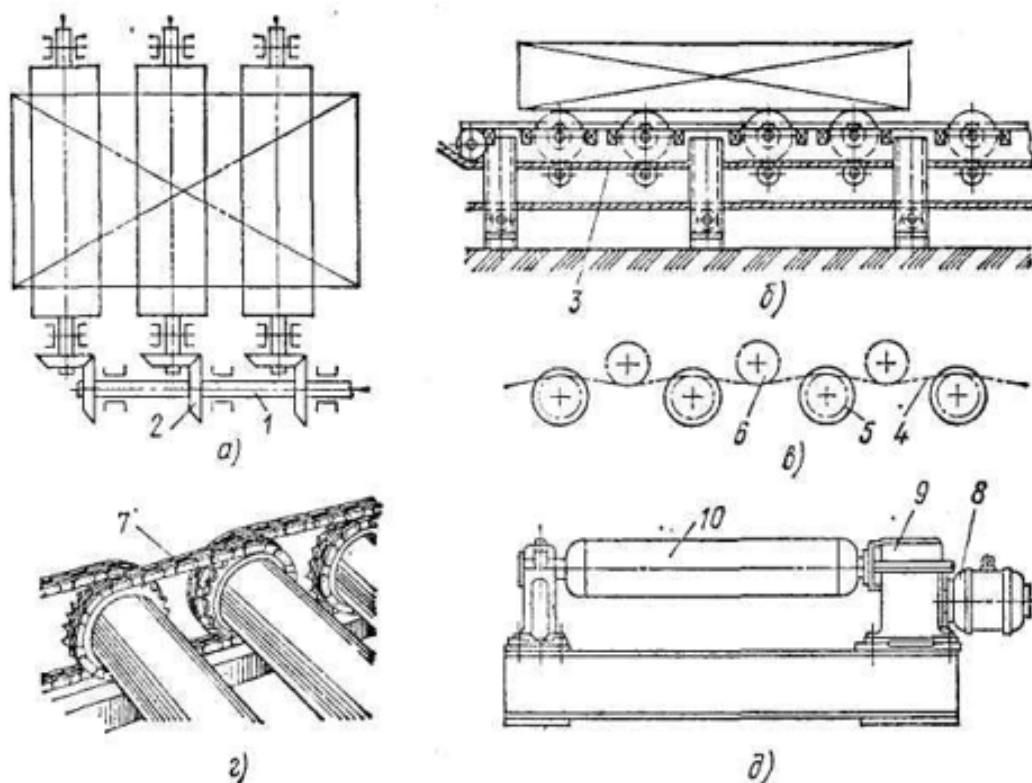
Привод вращения валков цепной передачи: а – от вала с коническими зубчатыми колесами; б – от канатной тяги; в – от одной общей приводной цепи; г – от цепной передачи от ролика к ролику; д – от индивидуального двигателя. 1 – вал; 2 – зубчатые колеса; 3 – стальной проволочный канат; 4 – цепь; 5 – звездочки; 6 – натяжные промежуточные звездочки; 7 – цепная передача; 8 – электродвигатель; 9 – редуктор; 10 – ролики
